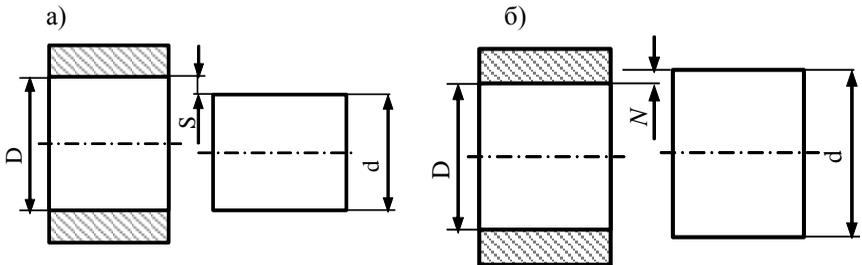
Соединения деталей: а – с зазором; б – с натягом
